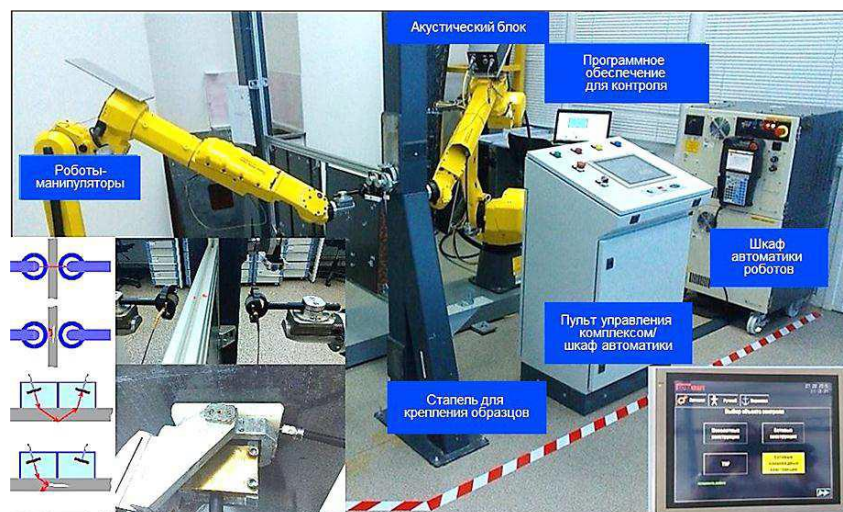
Автоматизированный комплекс для ультразвукового неразрушающего контроля качества деталей и агрегатов из ПКМ «МАК-ПКМ» [29]
